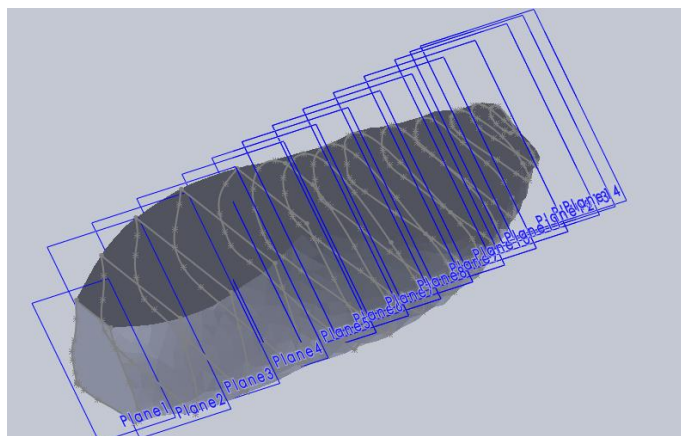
Conjunto de planos e respetivos sketches do contorno.
